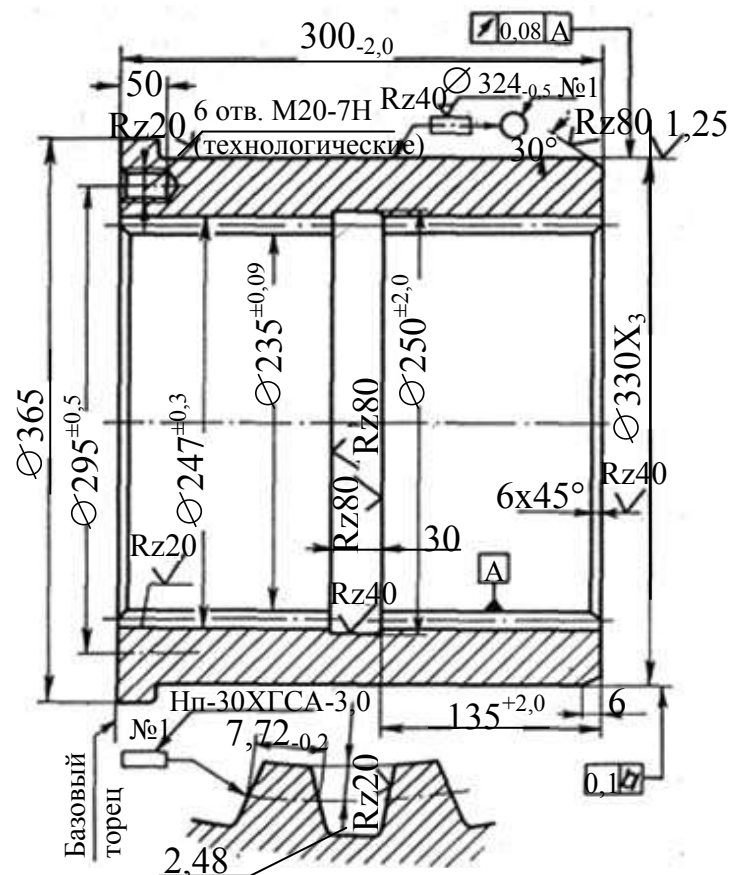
Ремонтный чертеж восстановления шлицевой муфты
